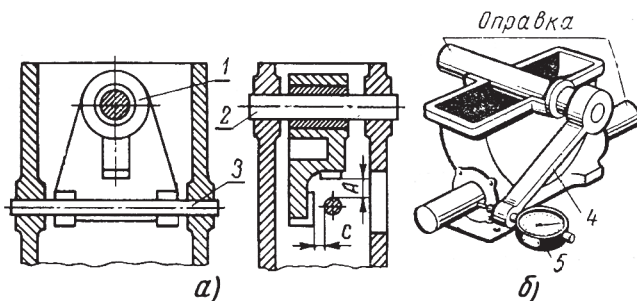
Схема проверки точности расположения отверстий в корпусе червячного редуктора:
